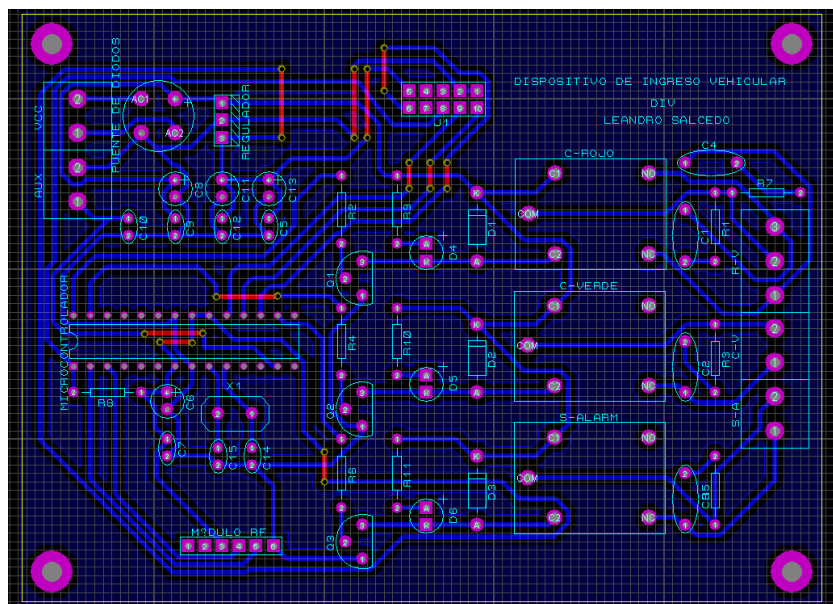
Diseño del PCB del Dispositivo de Ingreso Vehicular
